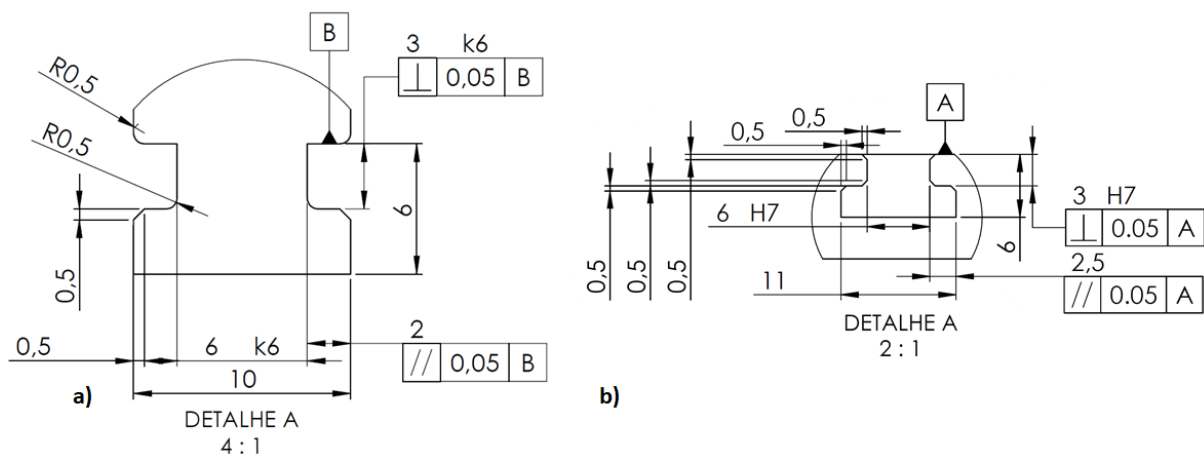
a) Dimensões e toleranciamento geométrico do olhal simples b) Dimensões e toleranciamento geométrico da Placa Traseira
